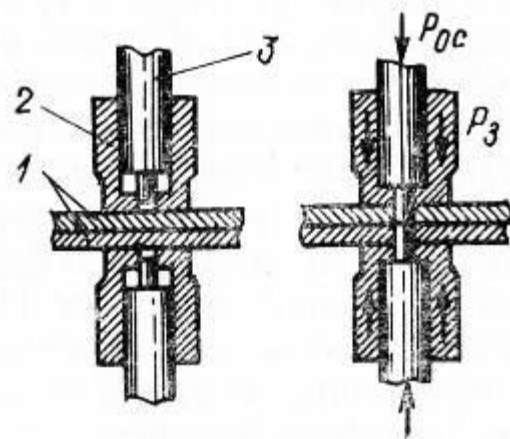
Схема точечной сварки с предварительным зажатием деталей:
